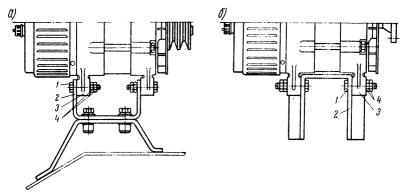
Крепление генератора Г290 (а) и генератора Г290-Б (б): 1 — болт; 2 — кронштейн двигателя; 3 — кронштейн генератора; 4 — гайки
